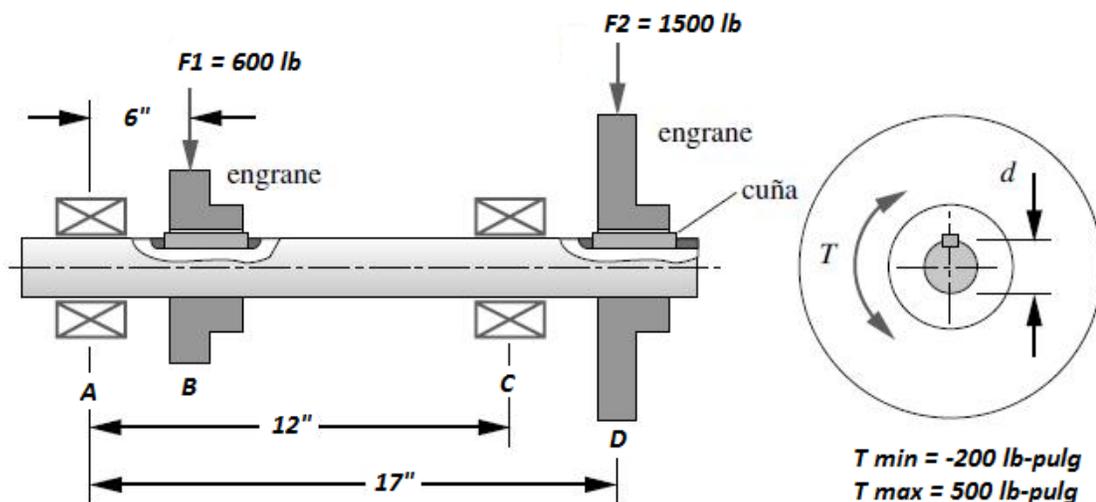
FIGURA. Eje de Transmisión con Engranes y Rodamientos
